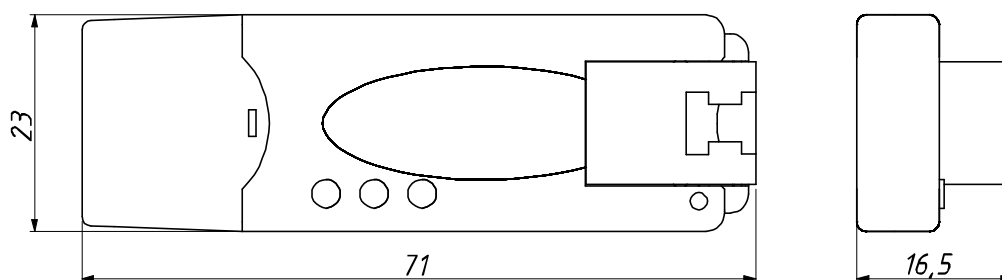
Габаритные размеры (с розеткой RJ-14)
